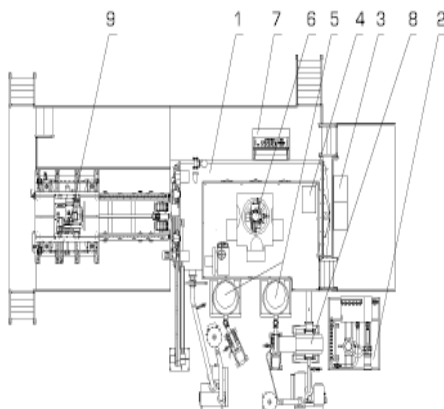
Внешний вид узлов установки: 1 – вакуумная камера; 2 – станция охлаждения; 3 – электрооборудование; 4 – источник питания; 5 – высоковакуумный блок; 6 – электронно-лучевая пушка; 7 – пульт управления; 8 – форвакуумный блок; 9 – сварочный манипулятор
